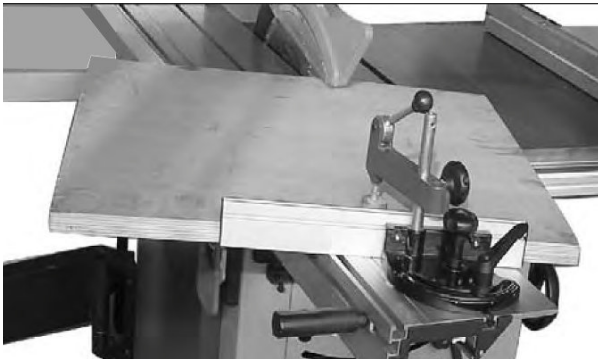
Gehrungsschnitt mit Winkelanschlag
